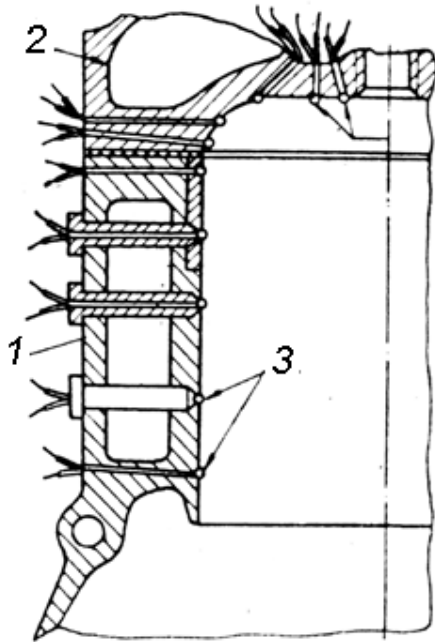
Цилиндр и головка двигателя Р-4, оборудованные термопарами:
